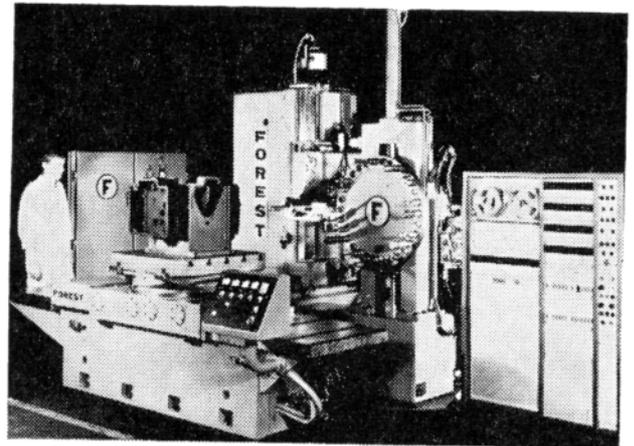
Bearbeitungszentrum mit 4-Achs-Streckensteuerung und Werkzeugwechselfmagazin für 30 Werkzeuge (Werkbild Ratier-Forest)
